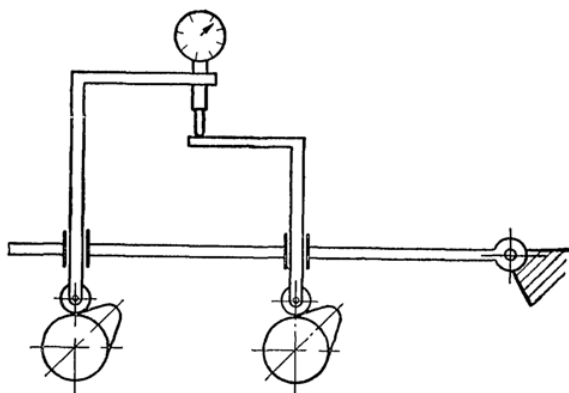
Схема контрольного прибора для проверки профиля кулачков распределительного вала
